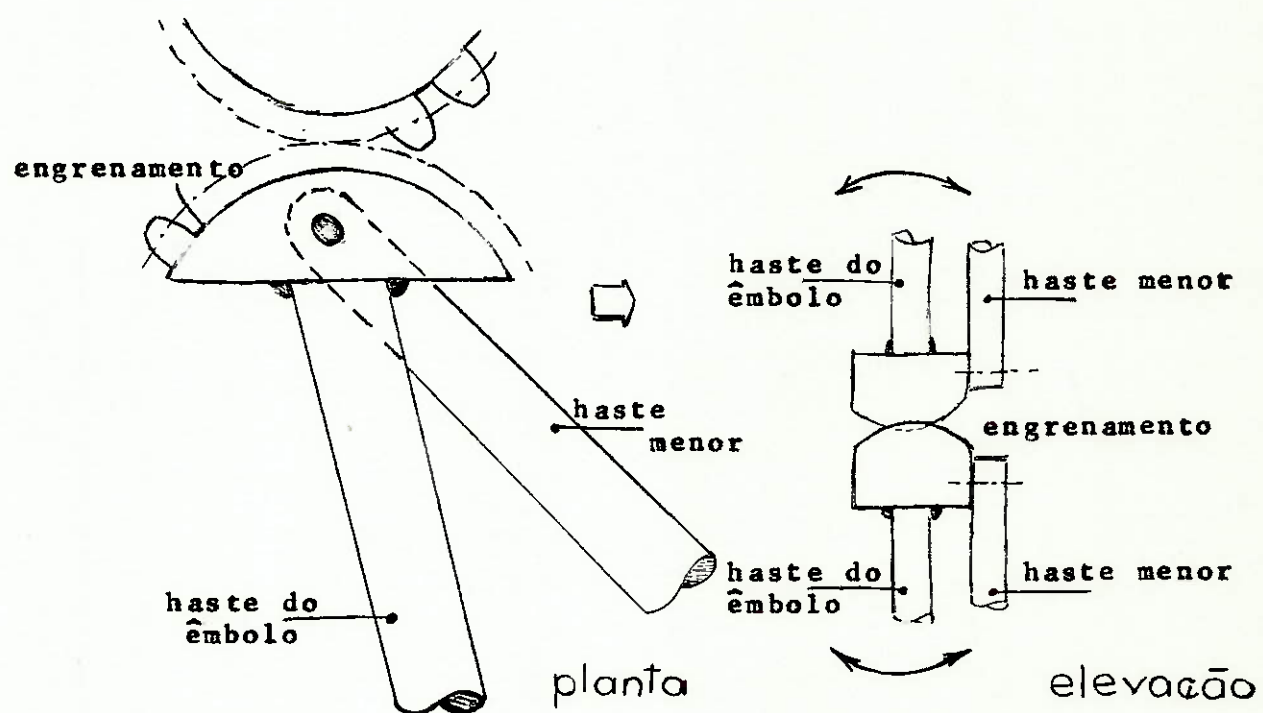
Detalhes para Montagem das Articulações do Dispositivo
